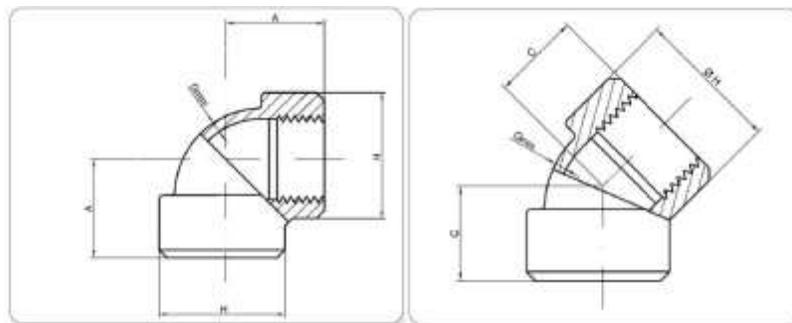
Codos roscados de 45° y 90°. Fuente: Catalogo Tubos y accesorios en acero al carbono soldado y sin soldadura Normas EN (DIN) y ASTM. Tubasol S.A
